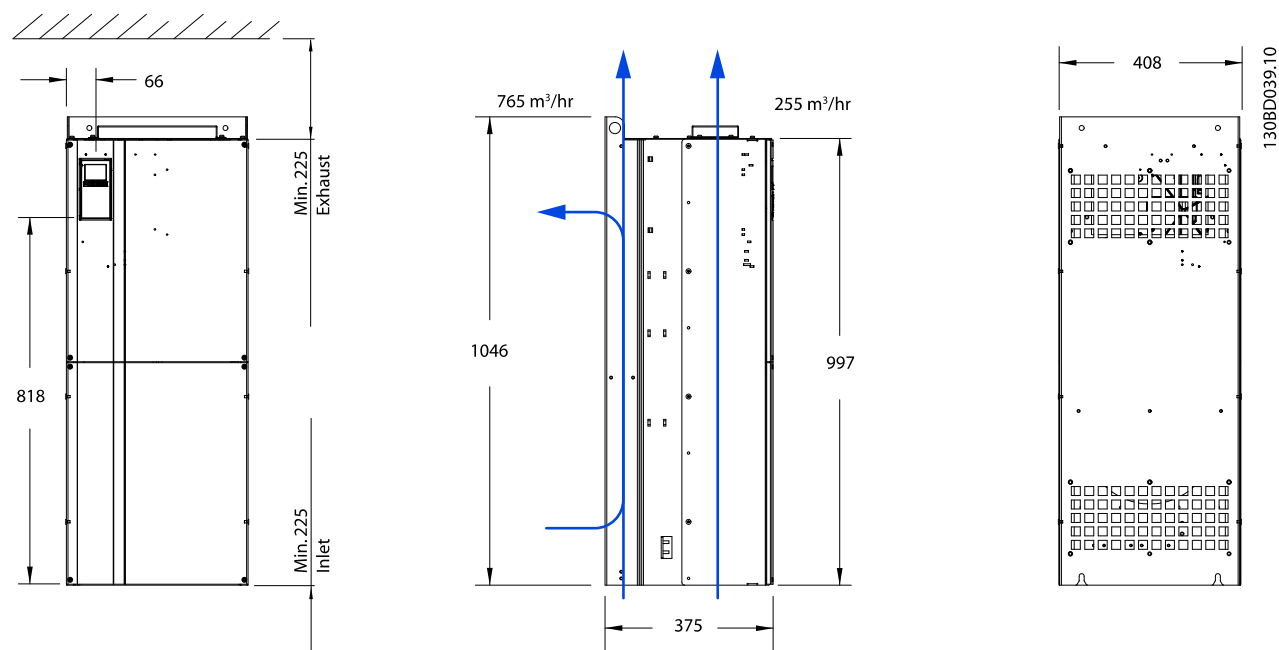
Gerätegröße 43 (Schaltschrankbefestigung)
